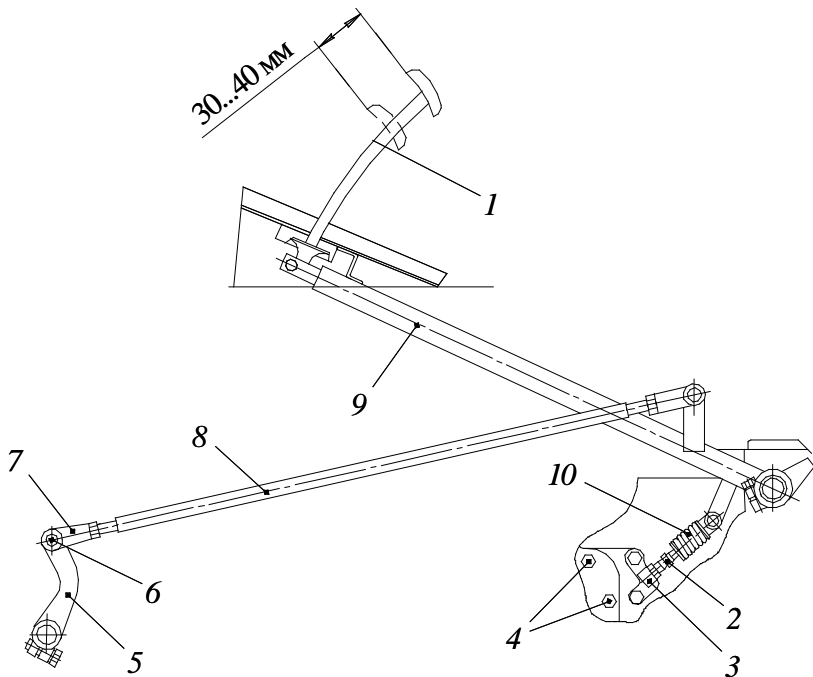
Проверка и регулировка сцепления: 1 – педаль; 2 – регулировочный болт сервоустройства; 3 – кронштейн; 4 – болты крепления; 5, 9 – рычаги; 6 – палец; 7 – вилка; 8 – тяга; 10 – пружина сервоустройства
